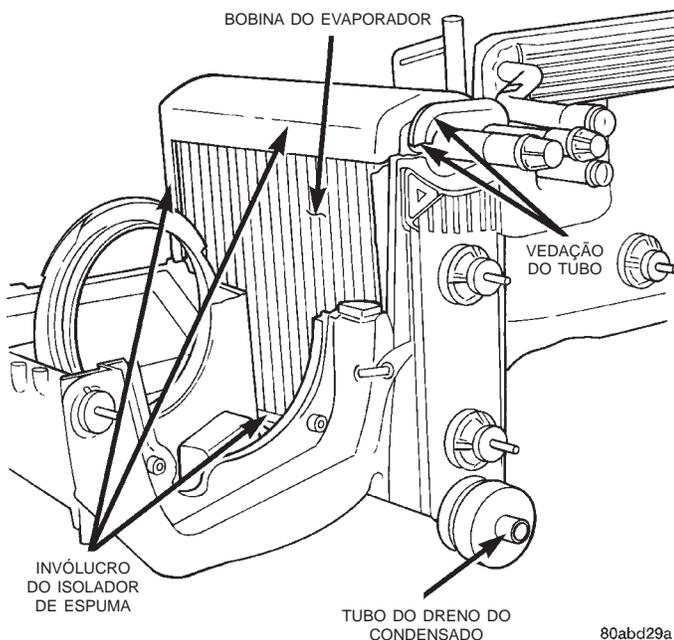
Remoção/Instalação da Bobina do Evaporador
